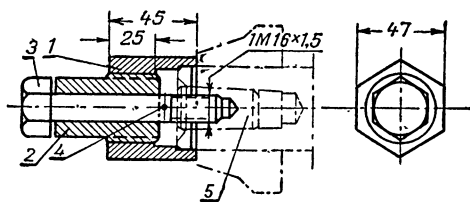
Съемник для выпрессовки конусного стопора из замыкающего пальца:
